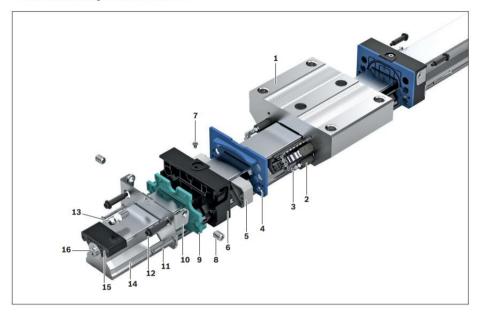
c: Detalle de patin y riel de deslizamiento EXPLOSIONADO
